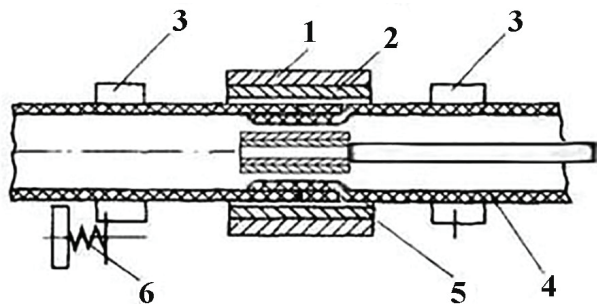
Схема сварки внахлест труб из ПТФЭ с применением оправок:
